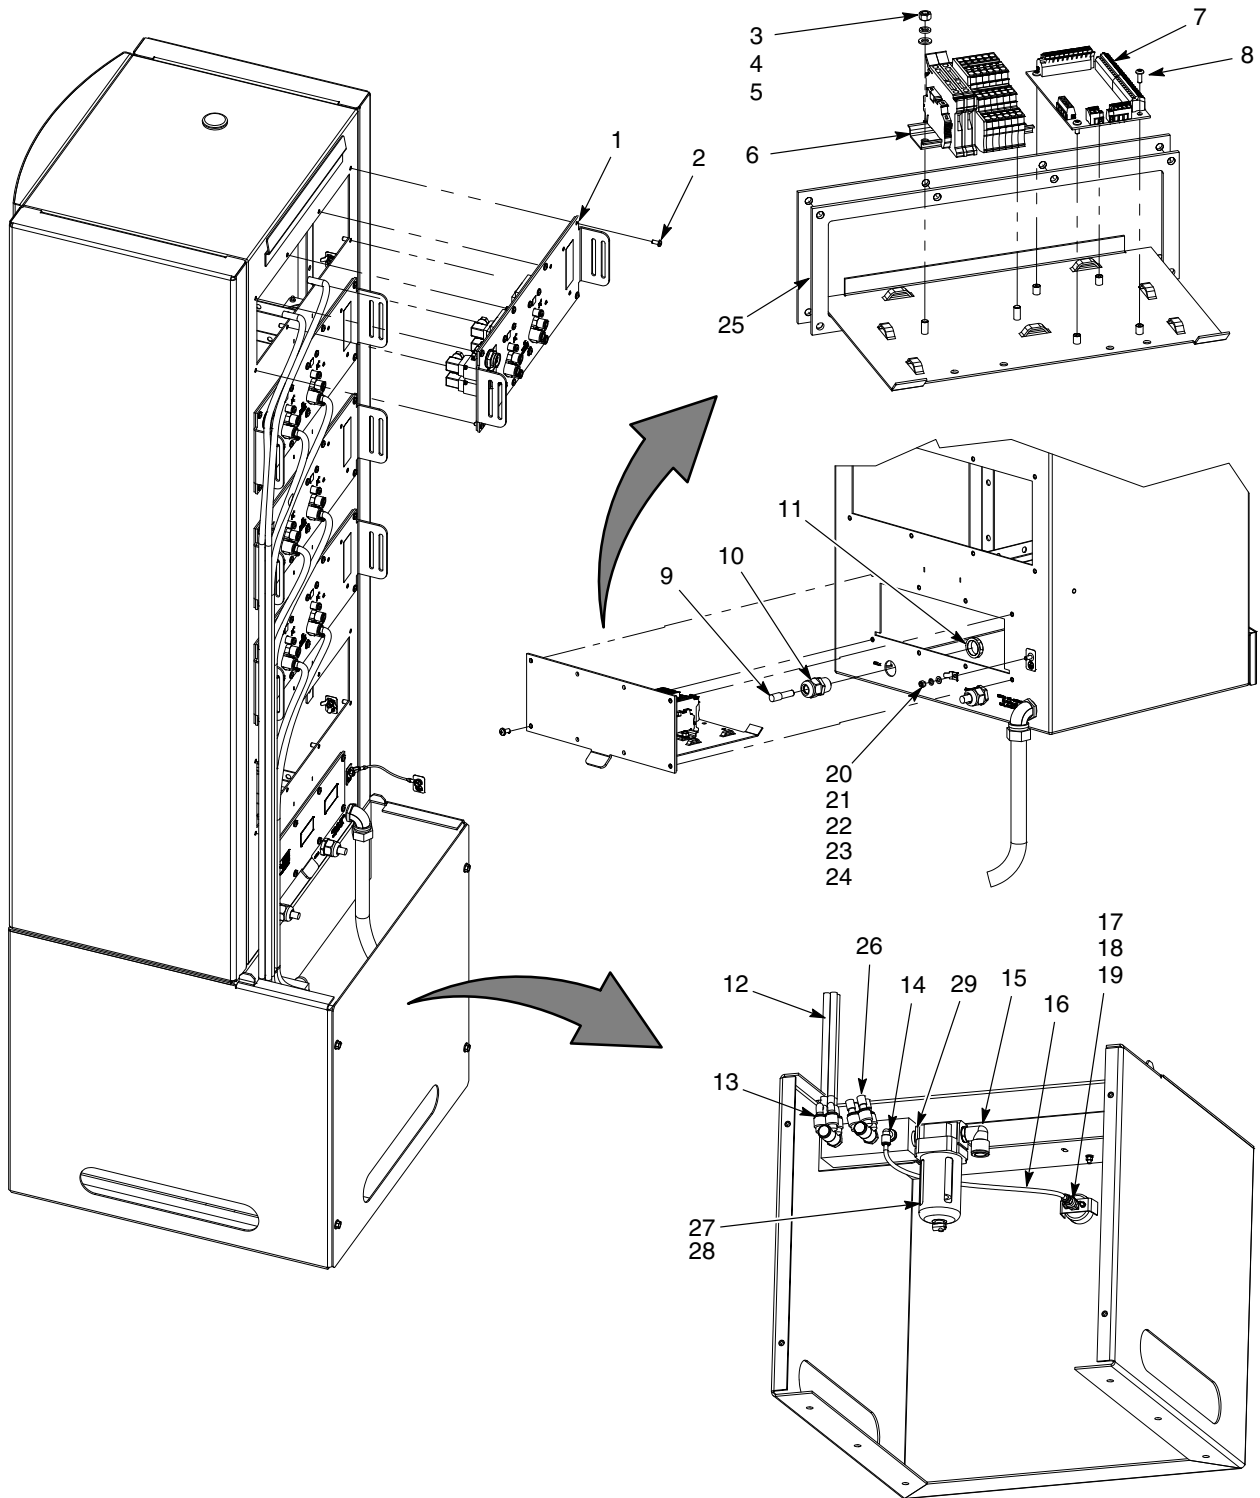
Rückwand, Steuerung für mehrere Pistolen
